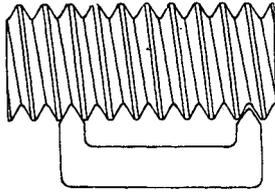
Gewindelehre zur Messung der Steigung. Rich. Weber u. Co., Berlin.
